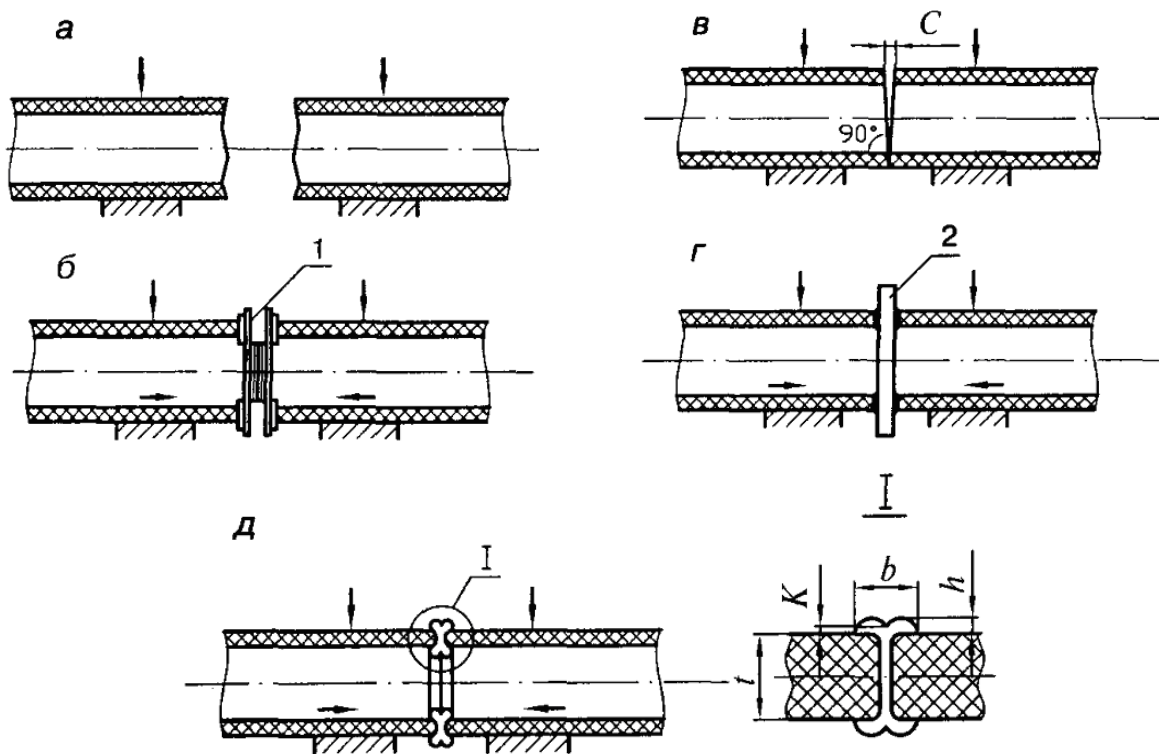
Последовательность процесса сборки и сварки встык труб из полиэтилена: *а* – центровка и закрепление в зажимах сварочной машины концов свариваемых труб; *б* – механическая обработка торцов труб с помощью «торцовки»; *в* – проверка соосности и точности совпадения торцов по величине зазора (*С*); *г* – оплавление и нагрев свариваемых поверхностей нагретым инструментом 2; *д* – осадка стыка до образования сварного соединения
